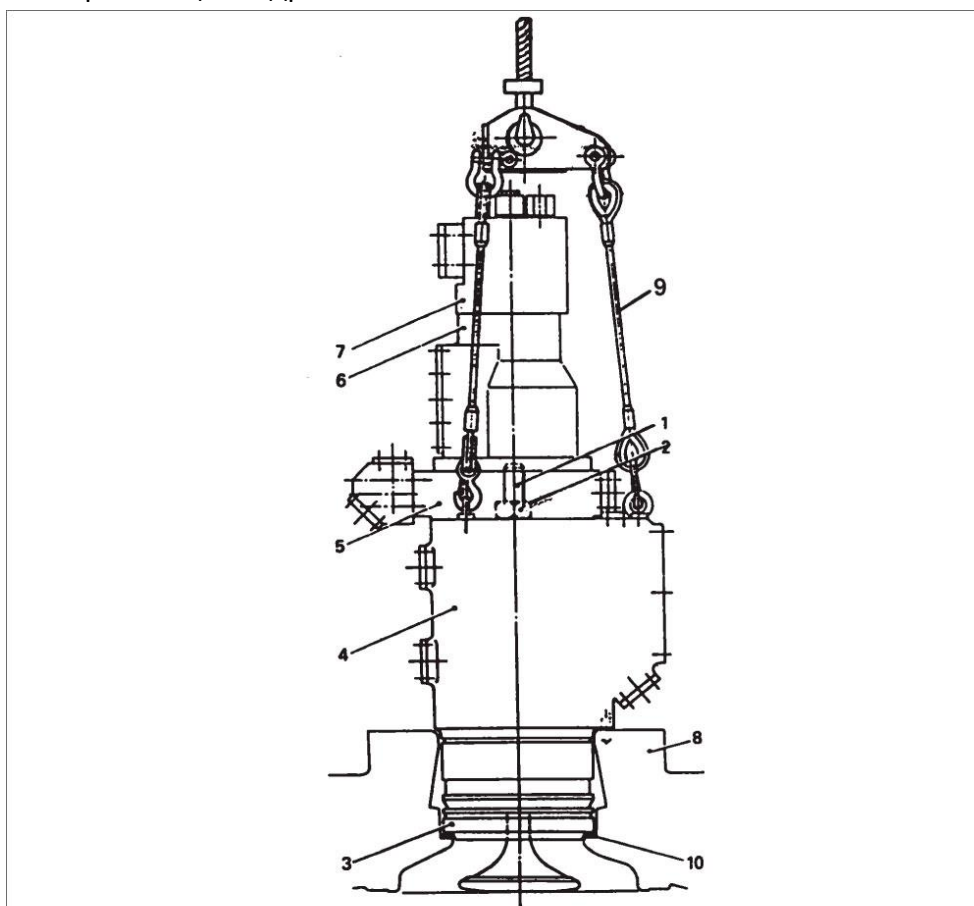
Схема установки приспособления для демонтажа выпускного клапана:
